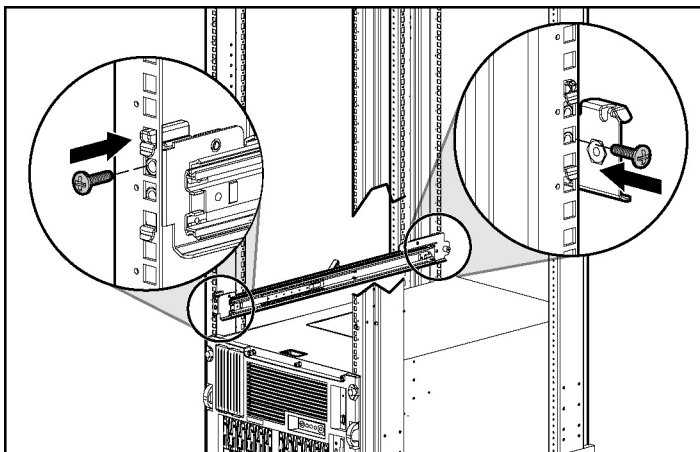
Einführen von Schrauben zum Befestigen der Rack-Schienenbaugruppe im Rack
